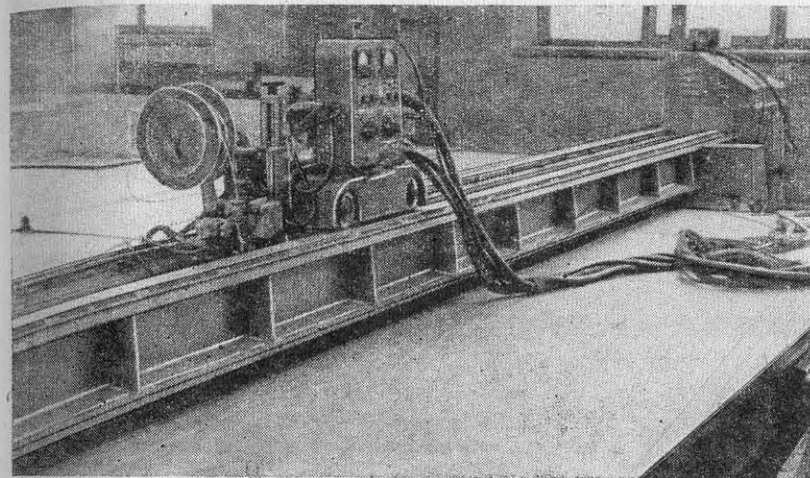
Стенд для автоматической сварки с установленным на нем автоматом типа АДСВ-2.
